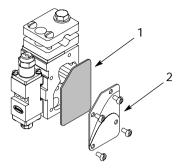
Position correcte du joint plat sur les pistolets étanches à l'eau
